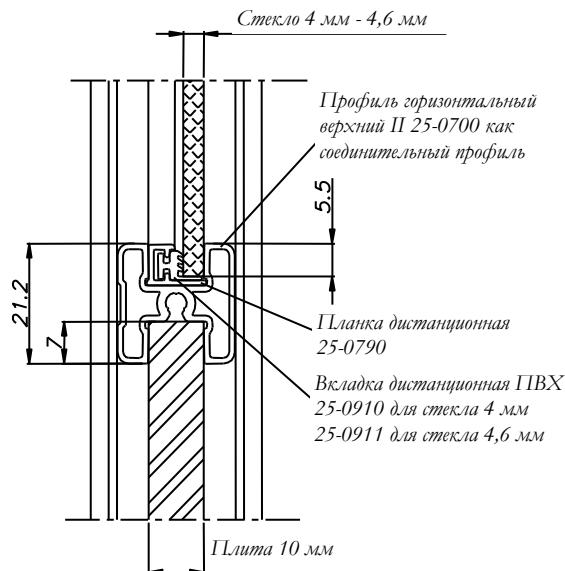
Схема деления дверей с вертикальными профилями AGAT II и LAZURYT II
